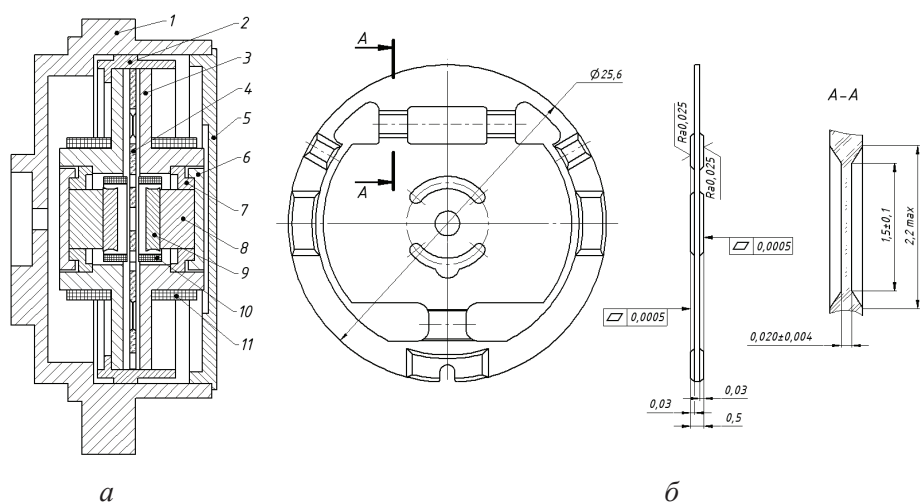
Конструктивное устройство маятникового акселерометра (а) и его пластины (б): 1, 3 — корпуса; 2 — кольцо; 4 — пластина; 5, 6 — крышки; 7 — втулка; 8 — магнит; 9 — полюсный наконечник; 10, 11 — катушки
